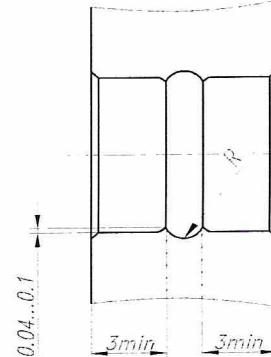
б – Однорядный уплотнительный кольцевой рельеф
